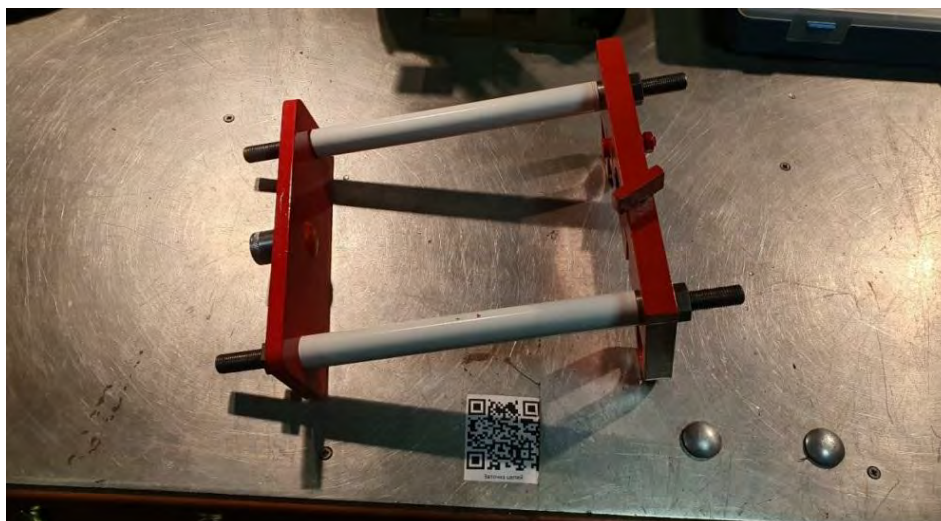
Приспособление с установленным ключом динамометрическим шкальным.
